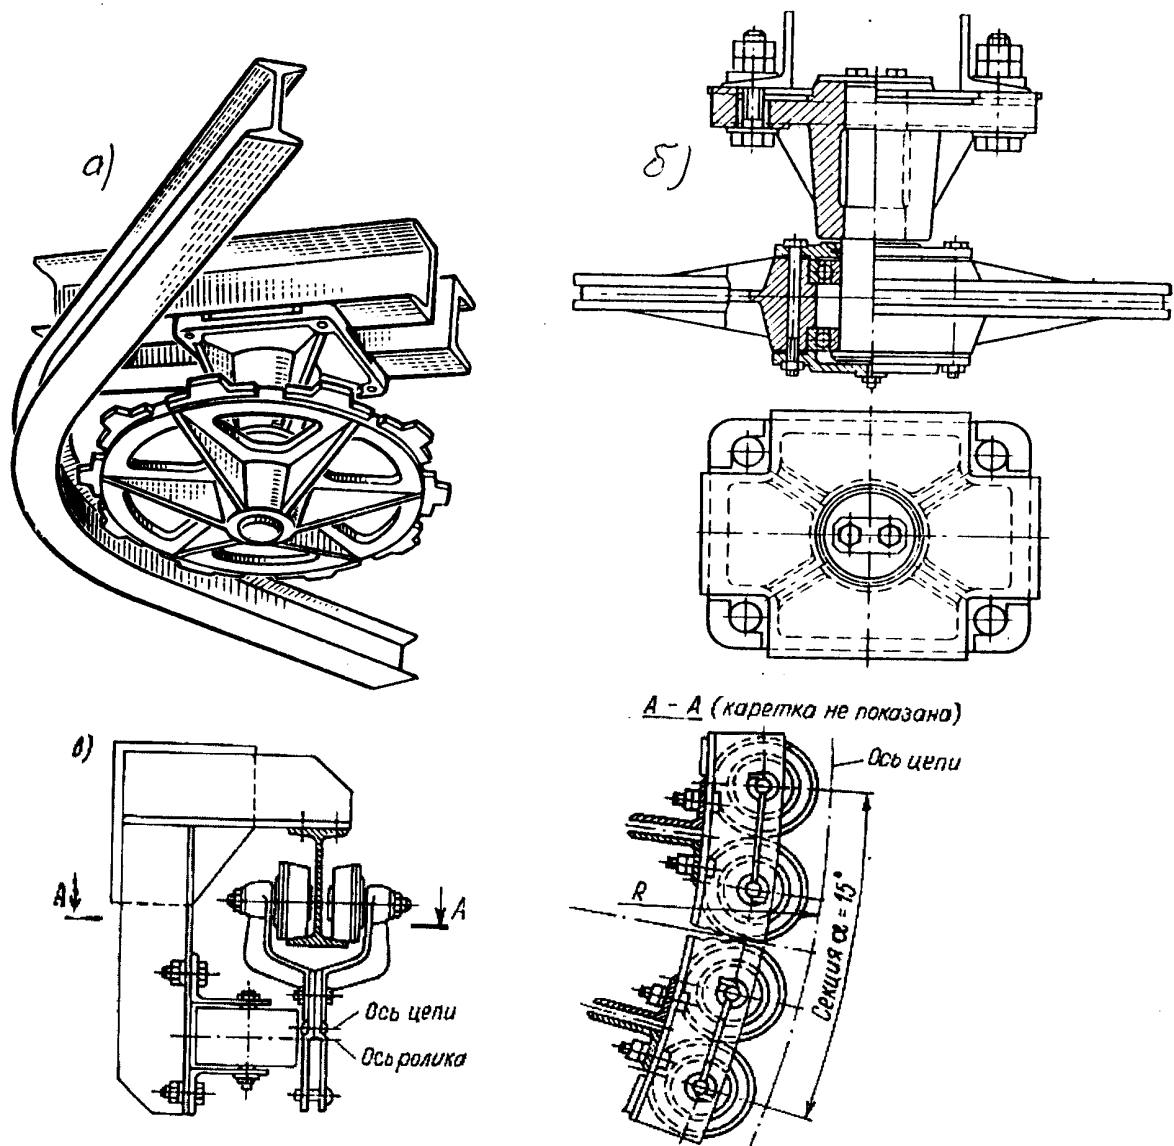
Поворотное устройство со звездочкой (а), блоками (б) и роликовой батареей (в)
